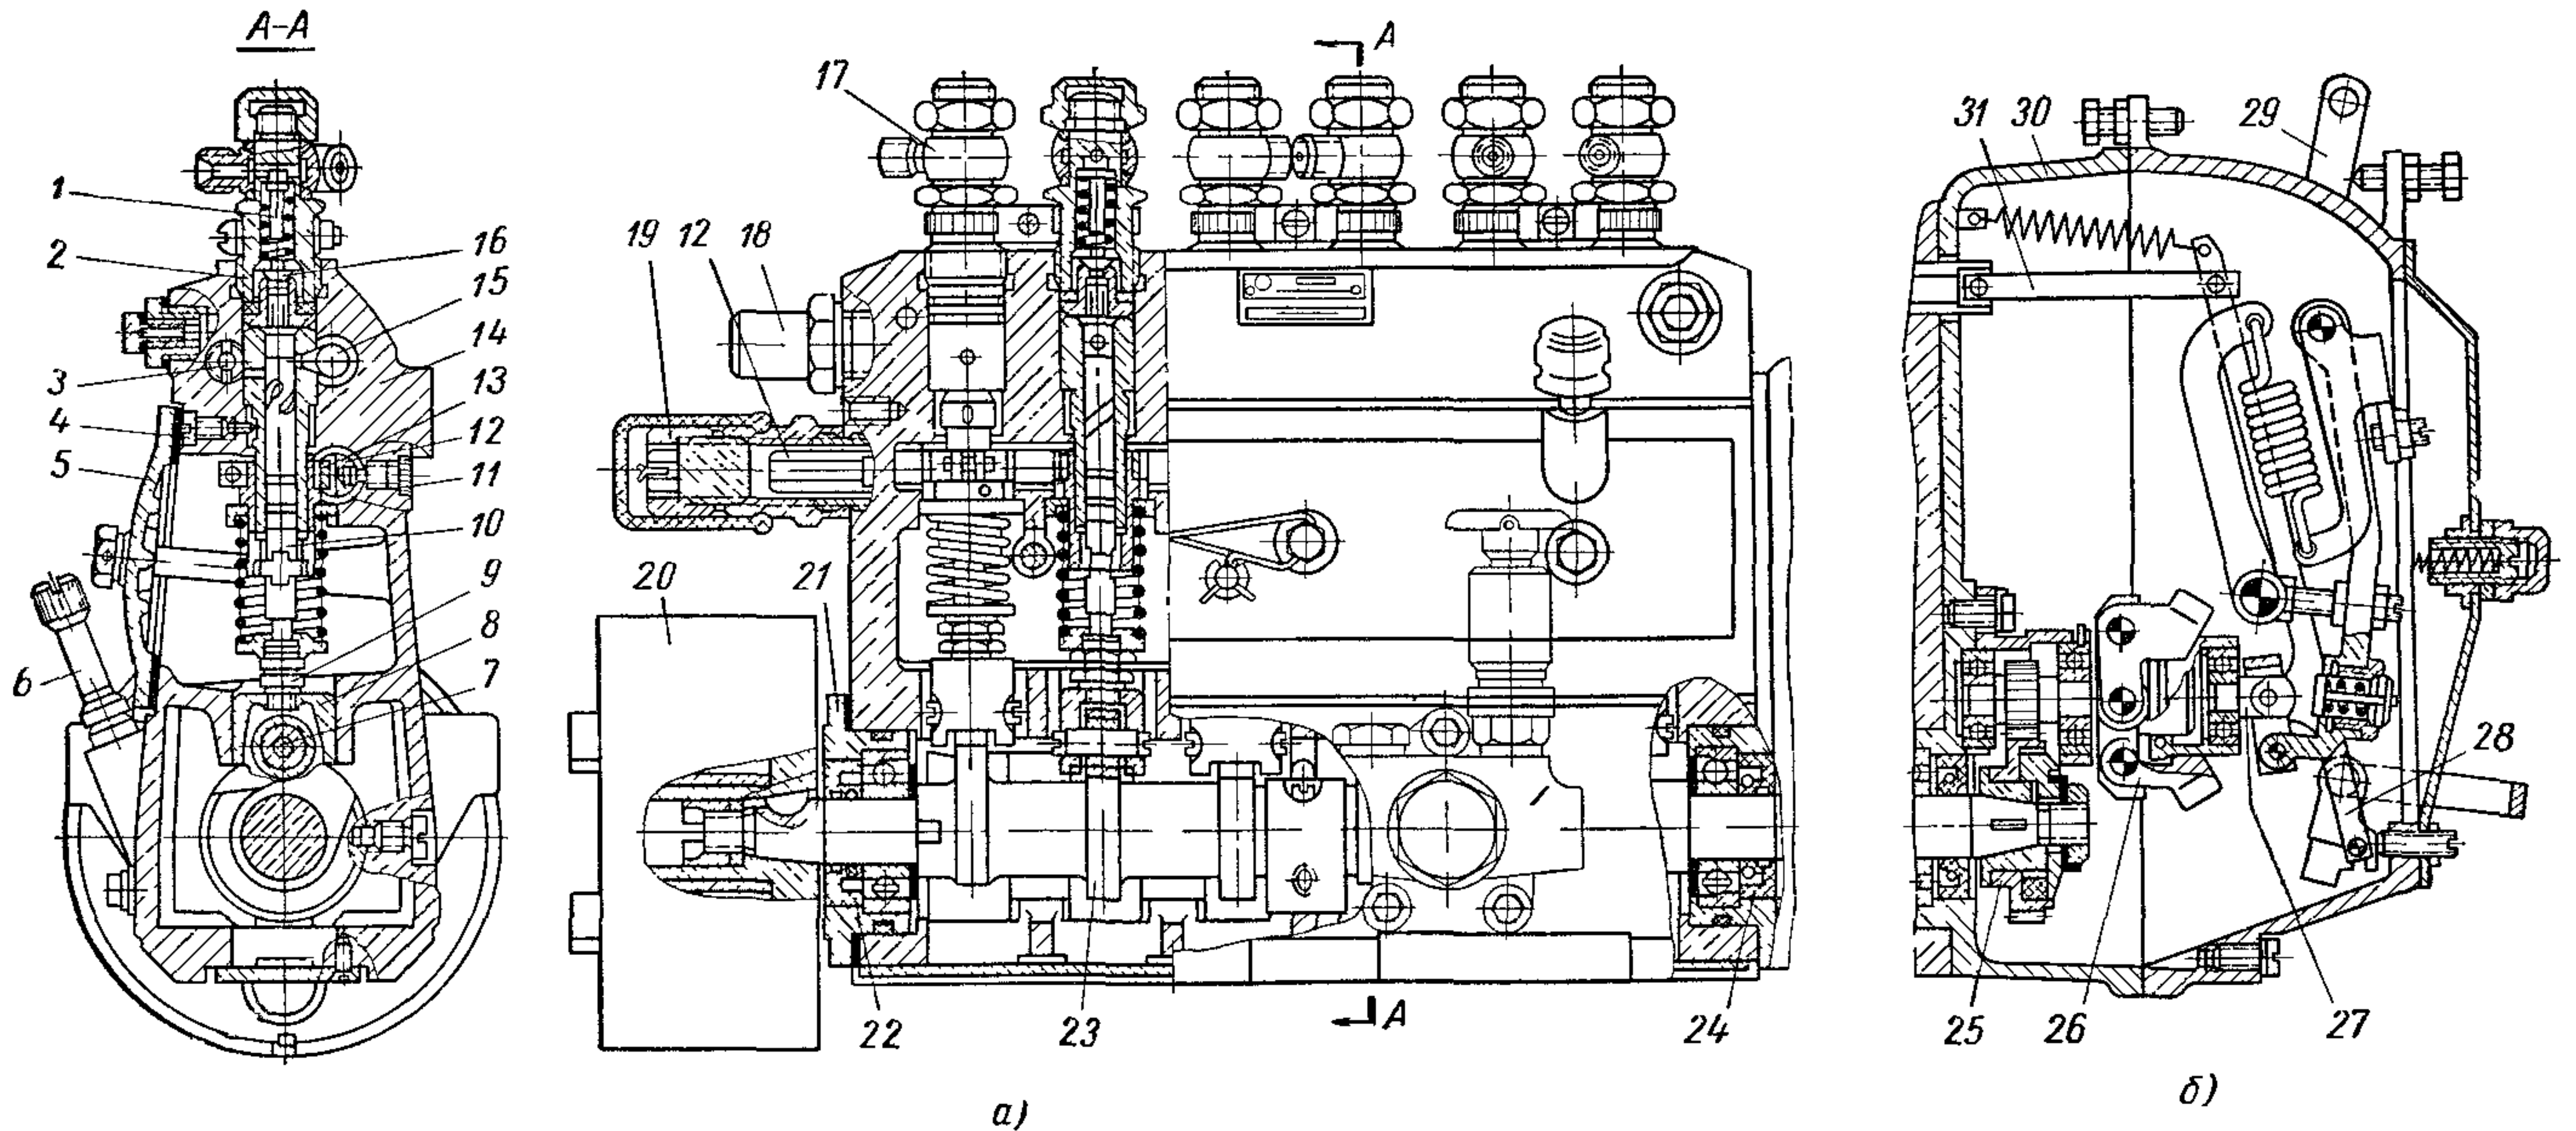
Шестисекционный топливный насос высокого давления с автоматической муфтой опережения впрыска и регулятором для двигателя ЯМЗ-236:
